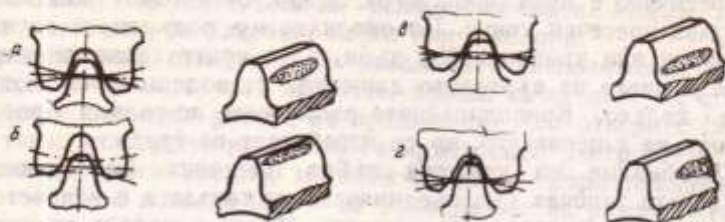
Зъбна предавка с цилиндрични колела
